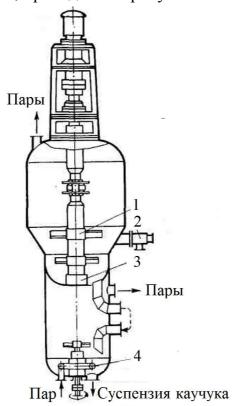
Двухступенчатый дегазатор: 1 – мешалка; 2 – крошкообразователь: 3 – опора вала; 4 – барботер
